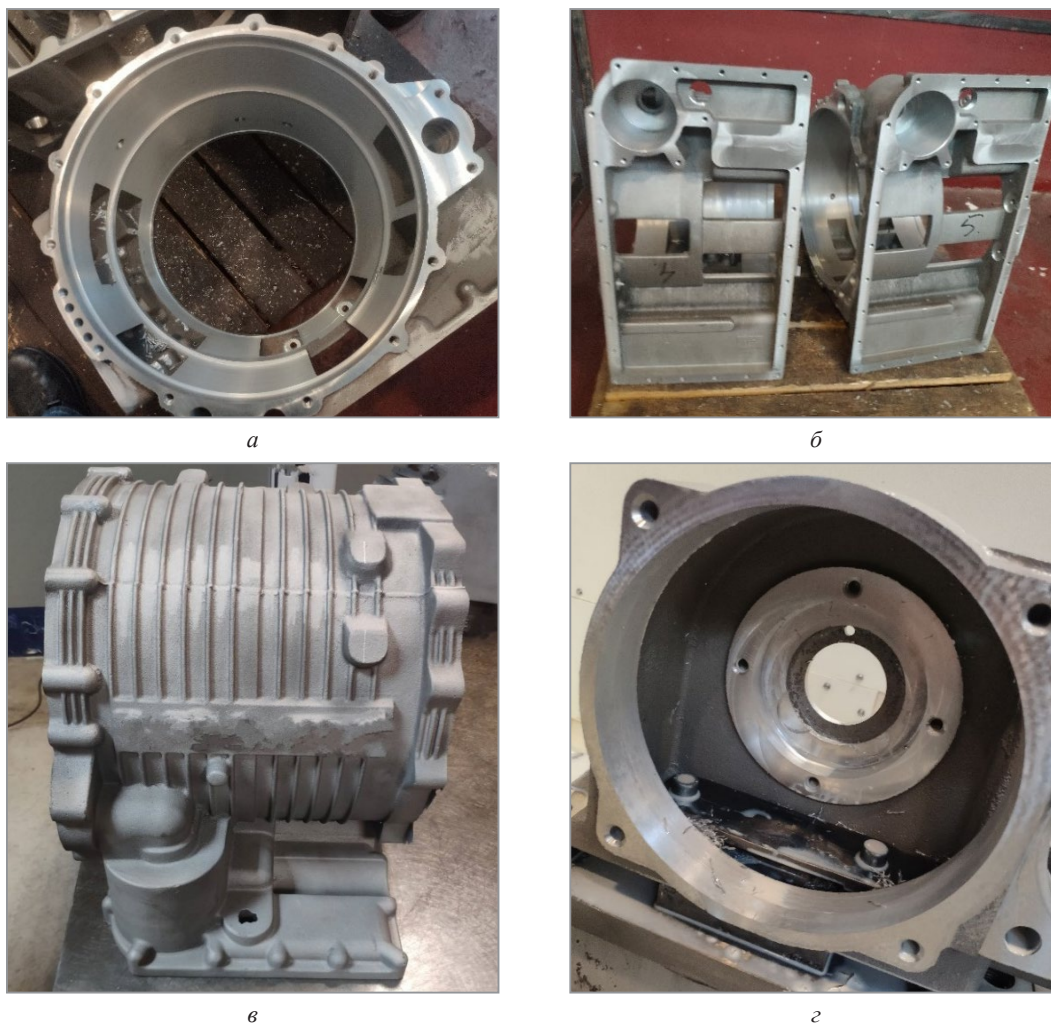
Общий вид отливок после предварительной механической обработки, получаемых по разработанной технологической схеме: а–в – отливка детали «Картер»; г – отливка детали «Корпус»
